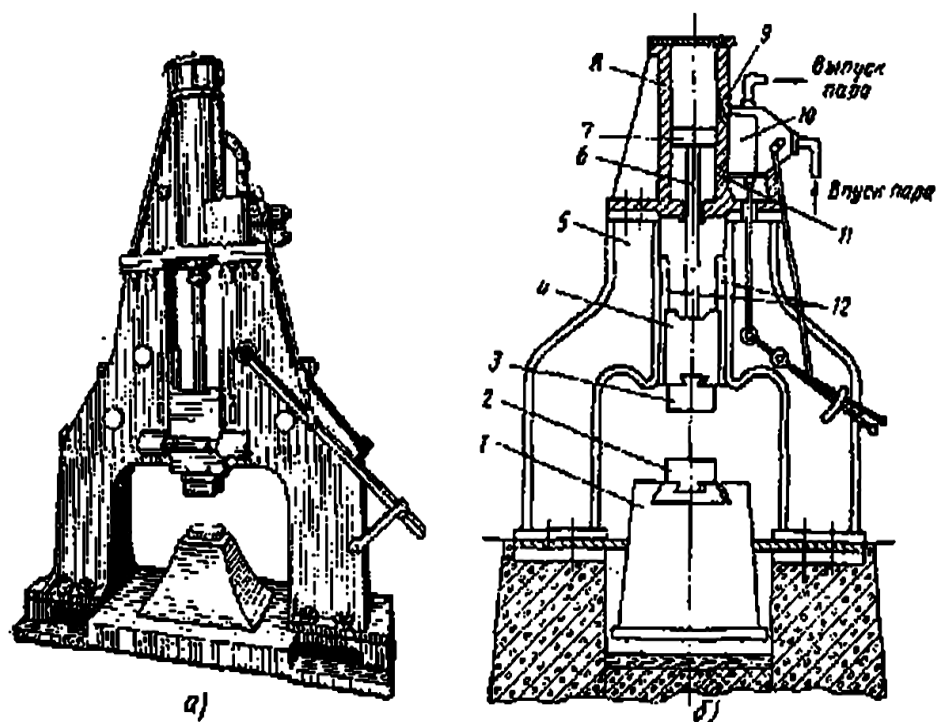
а - общий вид и б - схема паровоздушного молота: 1 – шабот; 2 – нижний боек; 3 – верхний боек; 4 – баба; 5 – станина; 6 – шток; 7 – поршень; 8 – цилиндр; 9 – канал; 10 – распределительное устройство; 11 – канал; 12 – направляющие.
